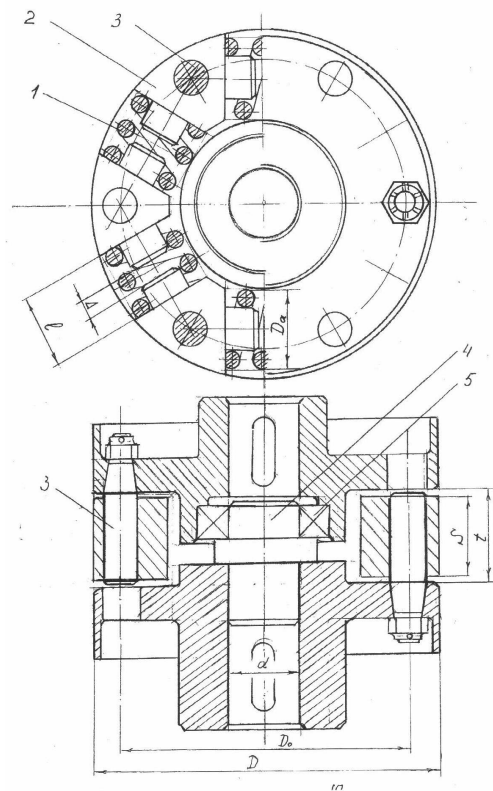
Пружна муфта: 1 - циліндрична витма пружна стиснення; 2 - несучий сегмент; 3 - палець; 4 - втулка; 5 - дворядний сферичний підшипник.
